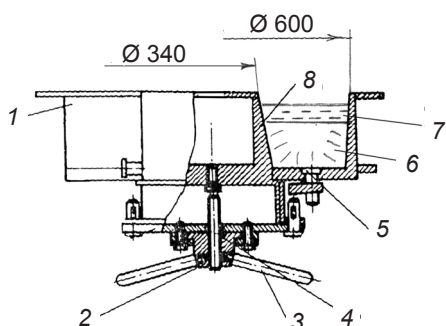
Схема получения колец методом ЭКЛ в кокиле с подвижным дорном: 1 – кокиль, 2 – гайка, 3 – штурвал, 4 – винт, 5 – толкатель, 6 – отливка, 7 – шлаковая шапка, 8 – дорн
